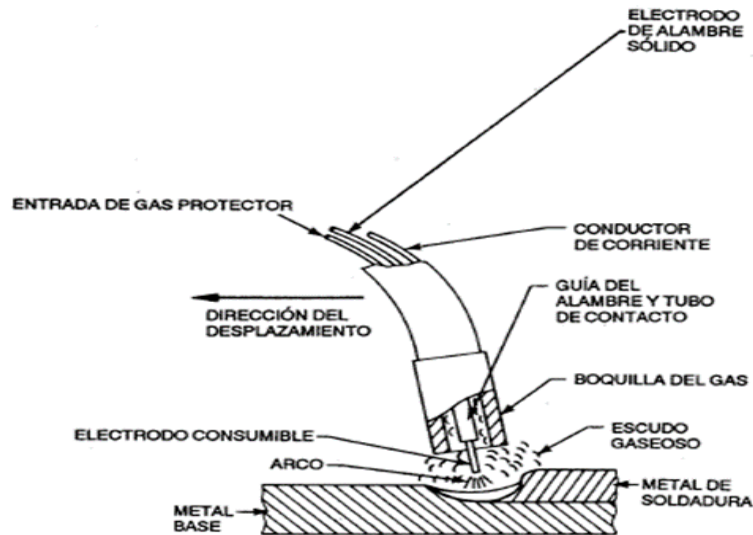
Descripción del Proceso de Soldadura GMAW [5].
